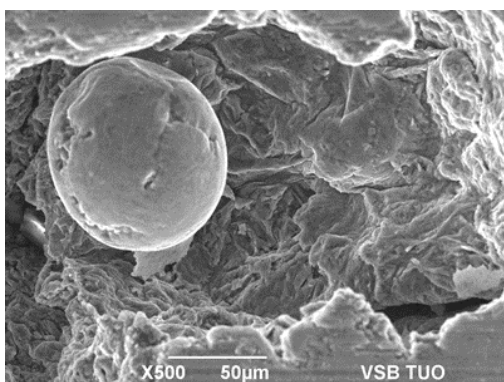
je pohled na povrch vady obr. 41b, obr. 42b je pohled na detailní povrch obr. 42a, obr. 43a je pohled na jiné místo povrchu obr. 41b, snímek 43b je pohled na detailní povrch obr. 43a.
